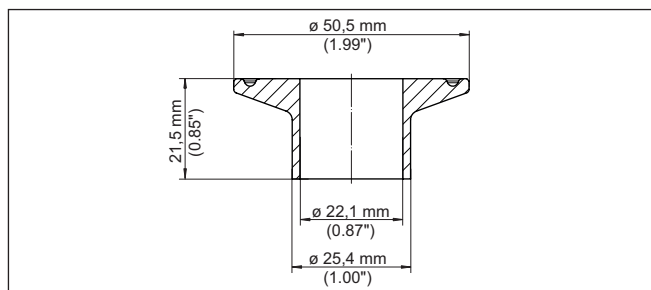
Dimensions raccord à souder Clamp 1" (DIN 32676, ISO 2852)
